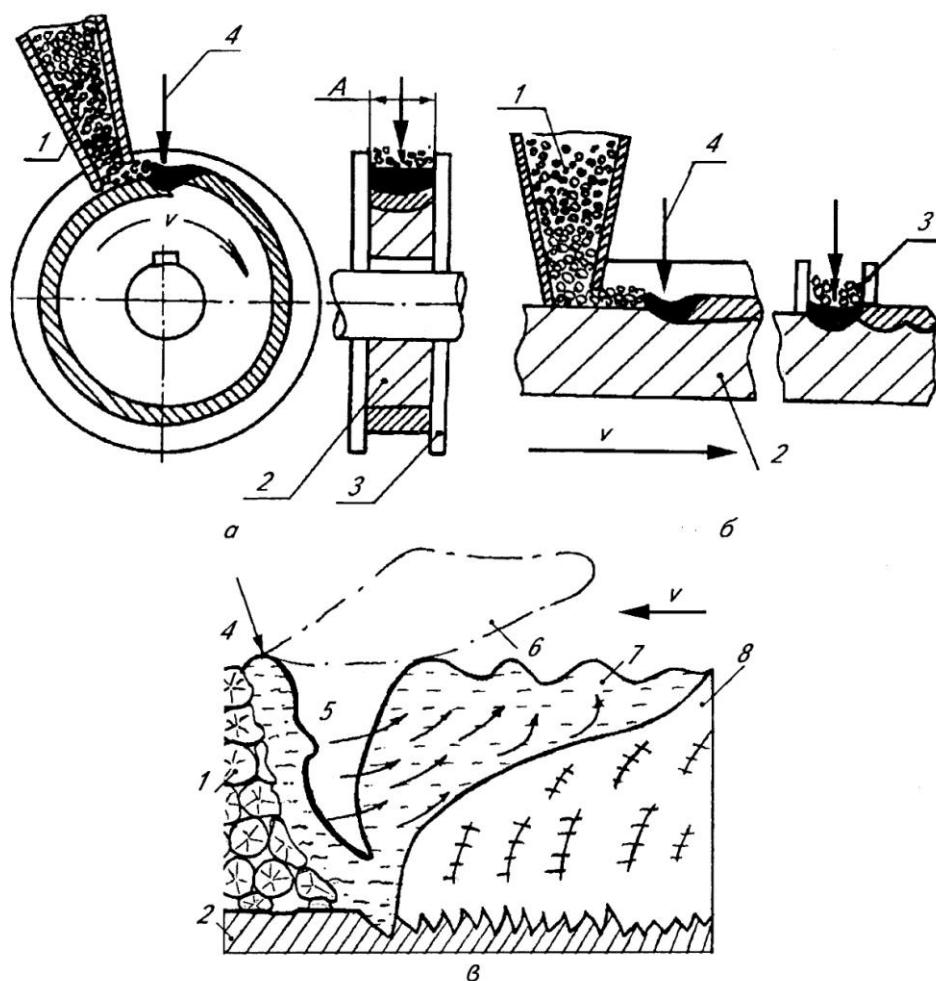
Схема радиальной (а) и торцевой (б) лазерной наплавки. В нижней части рисунка (в) показано продольное сечение сварочной ванны при лазерной наплавке порошкового сплава: 1 – порошковый наплавочный материал; 2 – обрабатываемая поверхность; 3 – кристаллизатор; 4 – излучение оптического квантового генератора; 5 – парогазовый канал; 6 – плазменный факел; 7 – сварочная ванна; 8 – наплавленный слой
